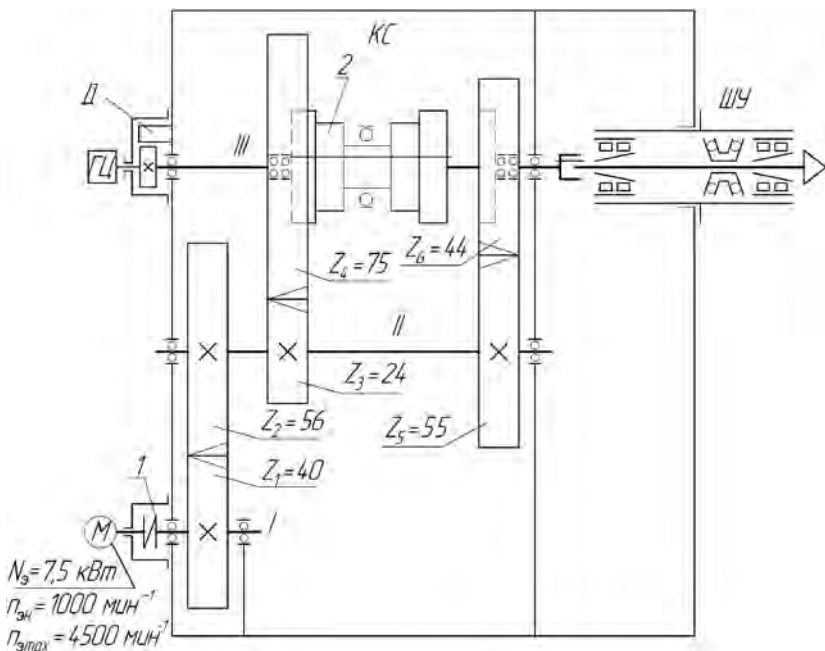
Кинематическая схема шпиндельной бабки с автономным шпиндельным узлом многоцелевого сверлильно-фрезерно-расточного горизонтального станка
